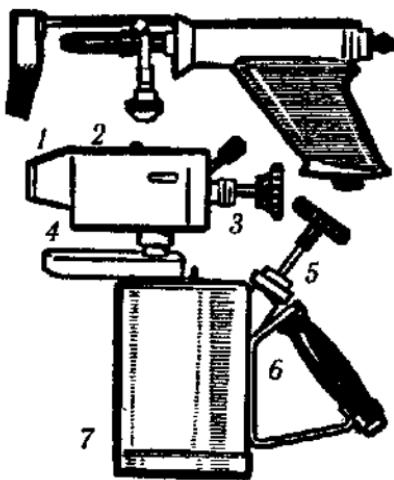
Паяльные лампы: 1 — горелка; 2 — воздушный баллон, 3 — рукоятка для регулирования пламени; 4 — нагревательный лоток; 5 — насос; 6 — ручка; 7 — бачок для горючего.
